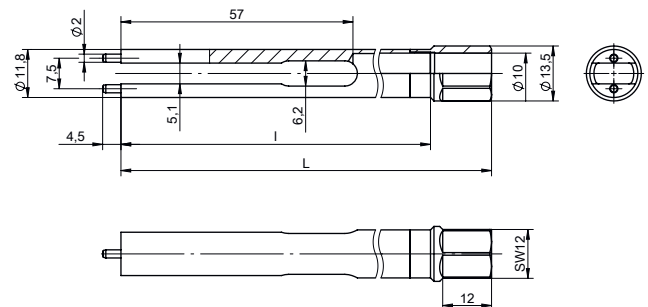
Montageschlüssel für Bohrung $\varnothing$ 12 SW12
